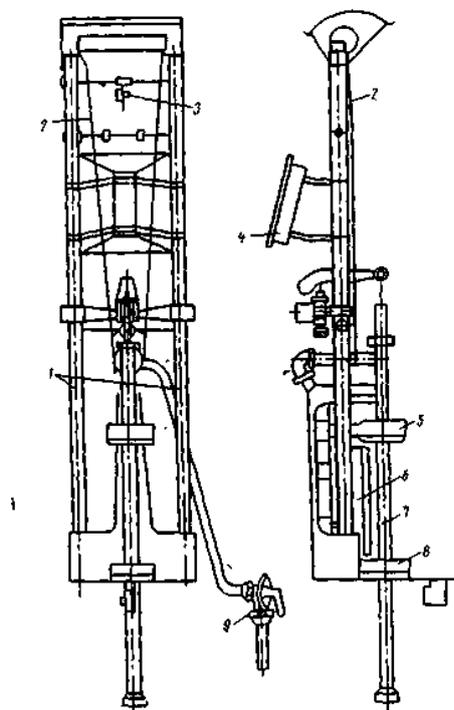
Устройство образования бумажной трубы и наполнительная система: 1 - стойки; 2 - направляющие для бумаги; 3, 10 - клапаны; 4 - бактерицидная лампа; 5 - верхнее формующее кольцо; 6 - нагреватель продольного шва; 7 - труба; 8 - нижнее формующее кольцо; 9 - трехходовой кран
